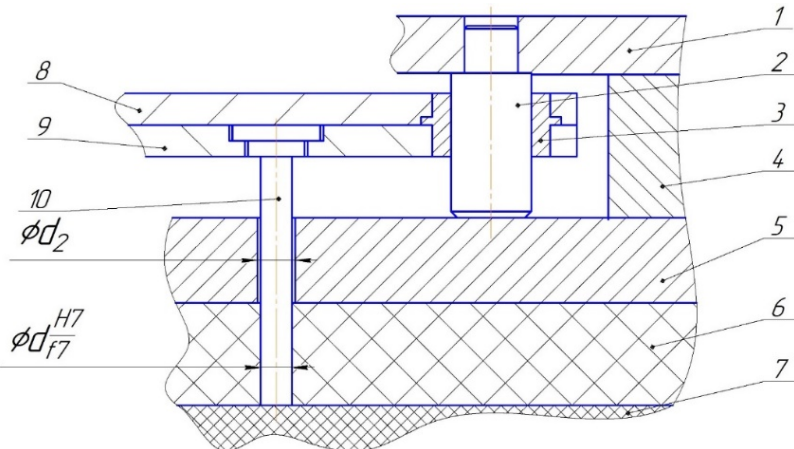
Схема выталкивающей системы пресс-формы с металлополимерной формообразующей частью: 1 – упорная плита; 2 – направляющая колонка; 3 – втулка под направляющую колонку; 4 – вспомогательная плита; 5 – направляющая плита выталкивателей (металлическая обойма); 6 – металлополимерная формообразующая часть пресс-формы; 7 – полимерное изделие полученное в пресс-форме; 8 – опорная плита; 9 – плита выталкивателей; 10 – выталкиватель
